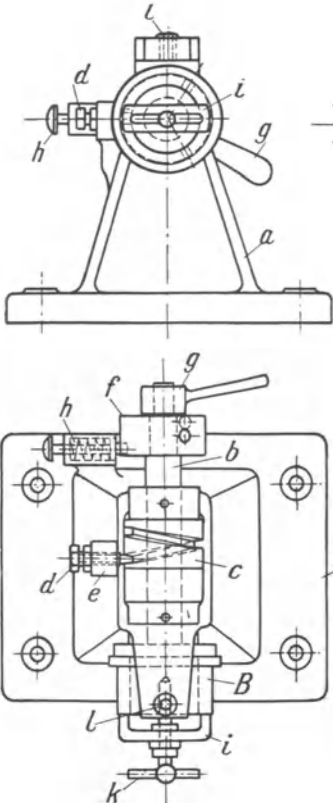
Bohrvorrichtung für kurze spiralig verlaufende Bohrungen auf Zylindermäntel.
